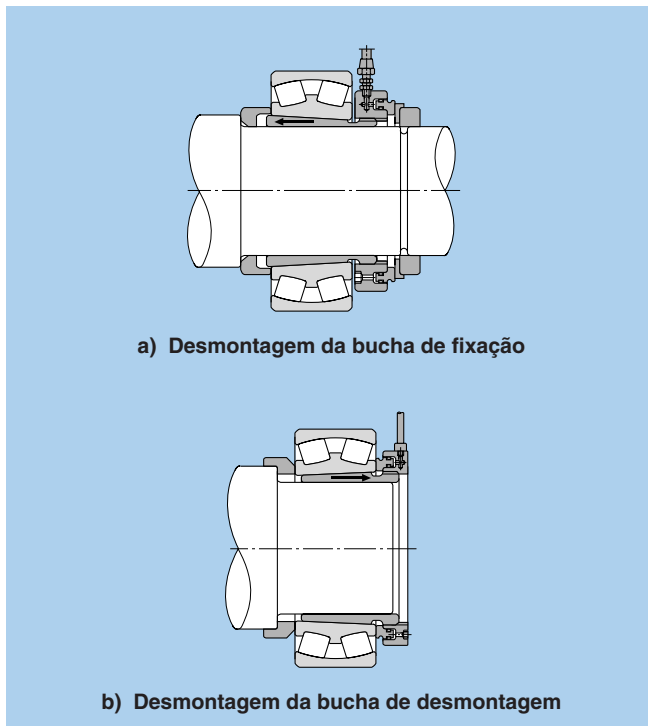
Desmontagem utilizando uma porca hidráulica
